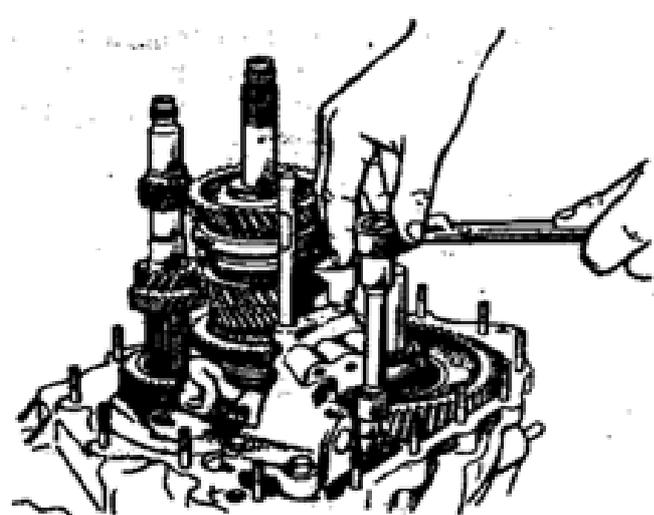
Отворачивание болтов крепления корпуса механизма переключения передач
